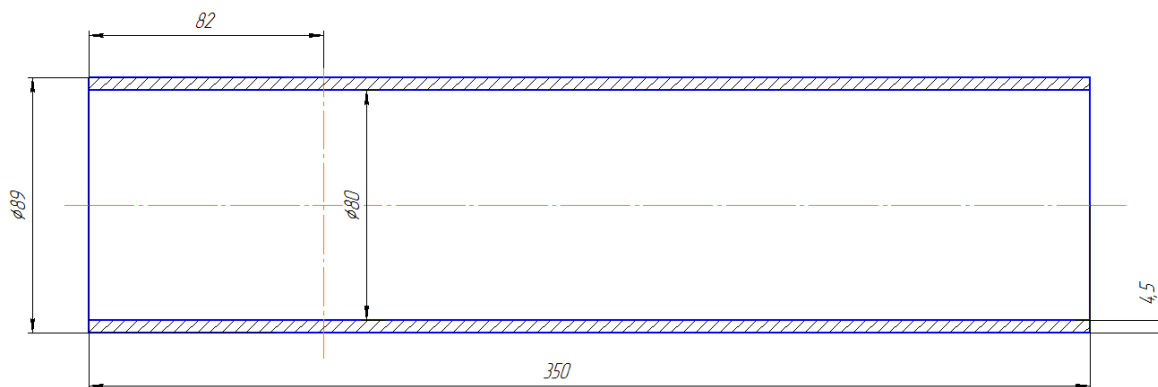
Креслення трубної заготовки для виготовлення днища балона
